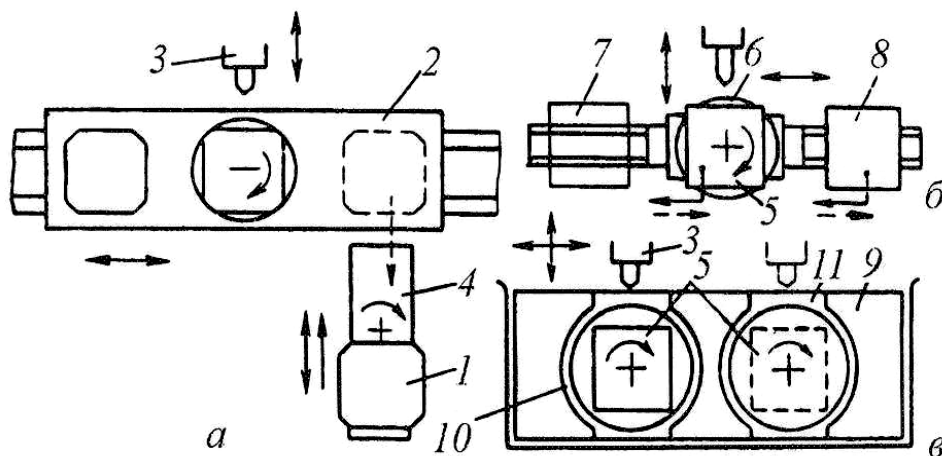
Способи кантування і зміни оброблюваних заготовок
